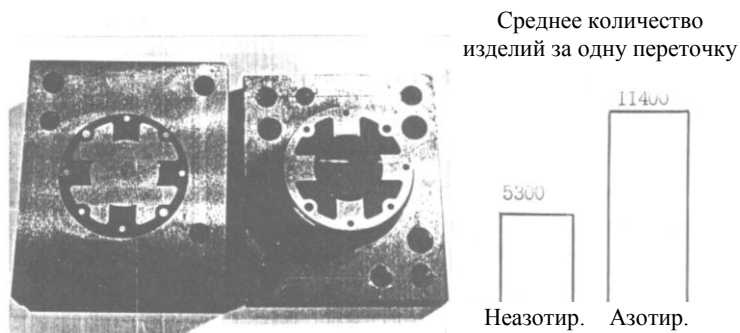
Вырубные штампы для изготовления пластин статора электродвигателя
